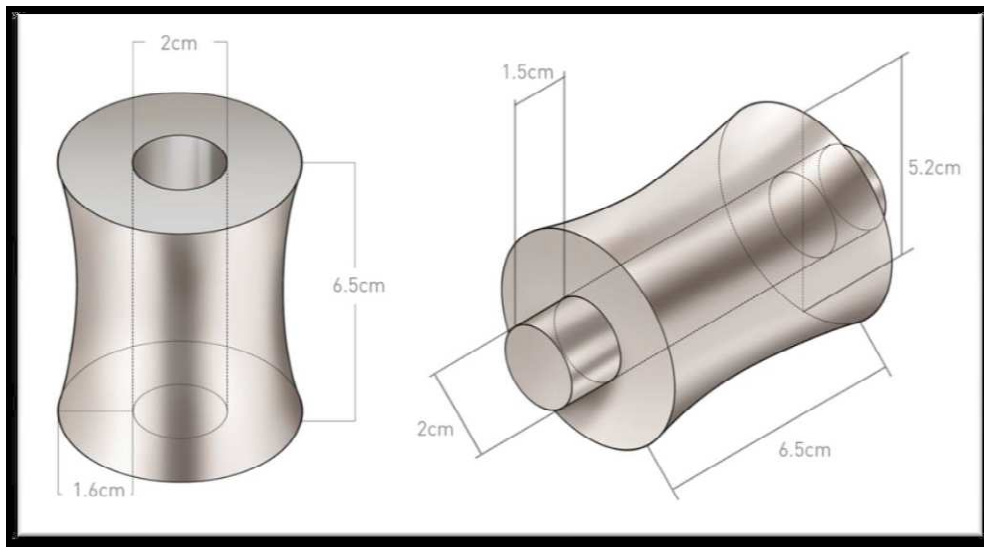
Dimensiones del rodillo para cáncamo de red de pesca.
